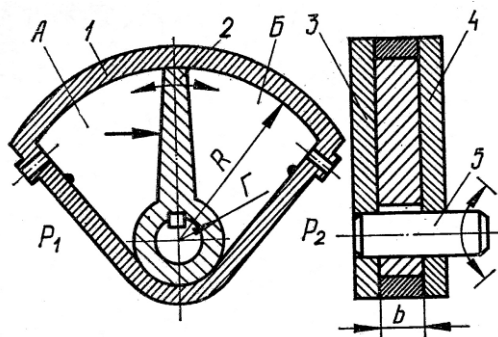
Пластинчатый поворотный гидродвигатель:
